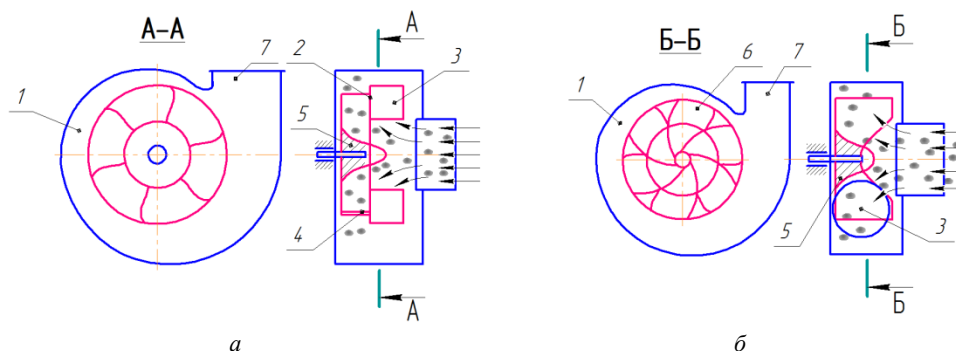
Радиальный вентилятор с консольными лопатками (а) и радиальный вентилятор с лопатками «двойного» профиля (б):
